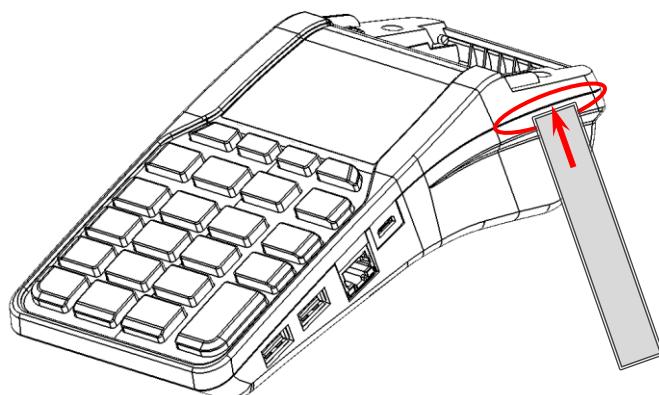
Место приложения усилий при отделении верхней части корпуса
